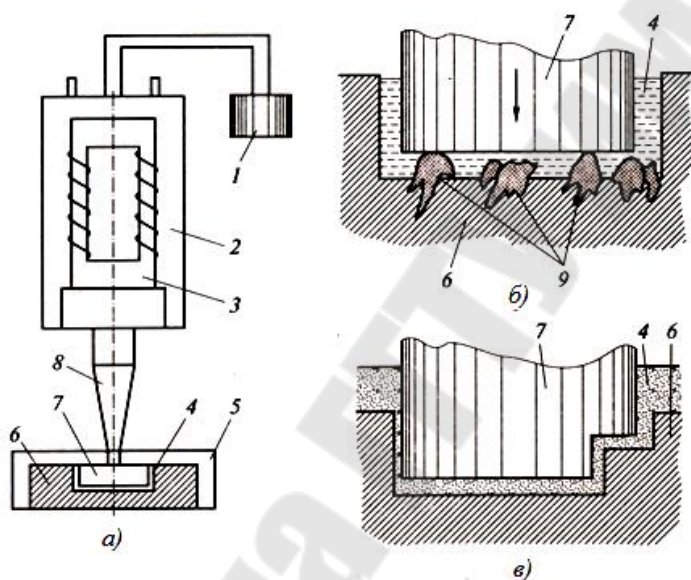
Схема ультразвуковой размерной обработки прошиванием (долблением): а – принципиальная схема ультразвуковой установки; б – схема съема материала при ультразвуковом прошивании; в – схема копирования профиля инструмента в заготовке: 1 – генератор тока повышенной частоты; 2 – корпус магнитосриктора с охлаждающей водой; 3 – магнитостриктор (пакет с обмоткой); 4 – зазор, заполненный суспензией абразива; 5 – ванна; 6 – обрабатываемая заготовка; 7 – инструмент; 8 – концентратор-волновод (трансформатор амплитуды); 9 – частички абразивных зерен
